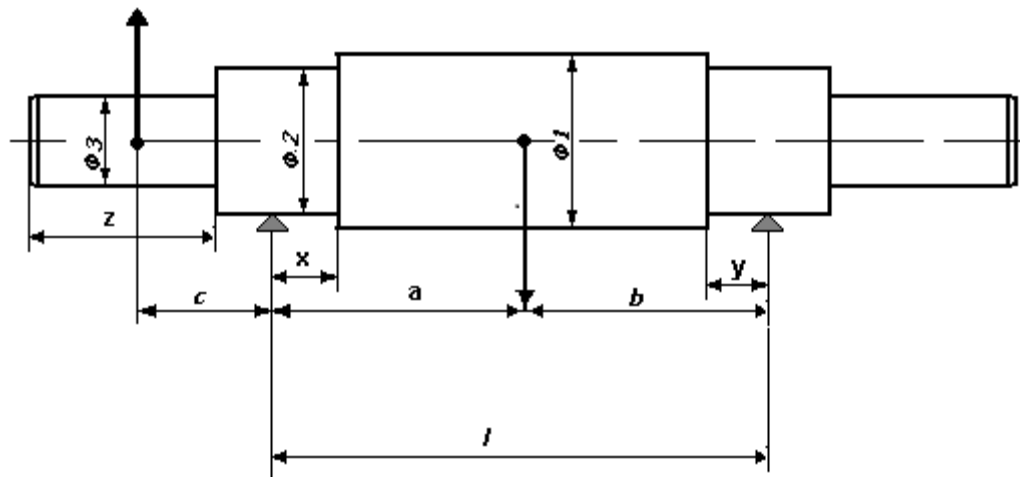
Конструкция и основные размеры вала для механического расчёта
